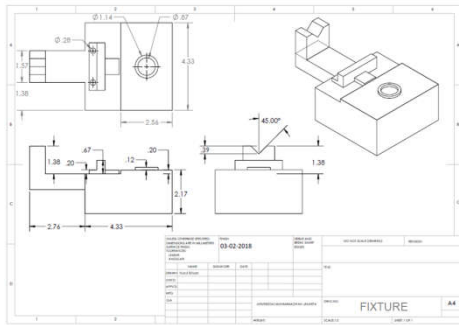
Fixture proses *sleeve install* sebelum perbaikan.
